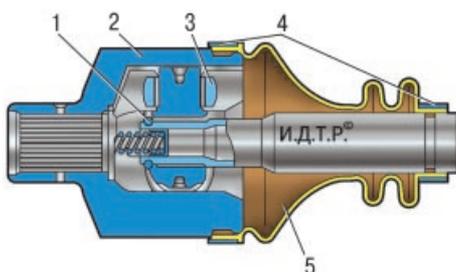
Правый внутренний шарнир равных угловых скоростей: 1 – стопорное кольцо; 2 – корпус шарнира; 3 – ролик трехшиповой ступицы; 4 – хомуты крепления чехла; 5 – чехол шарнира
